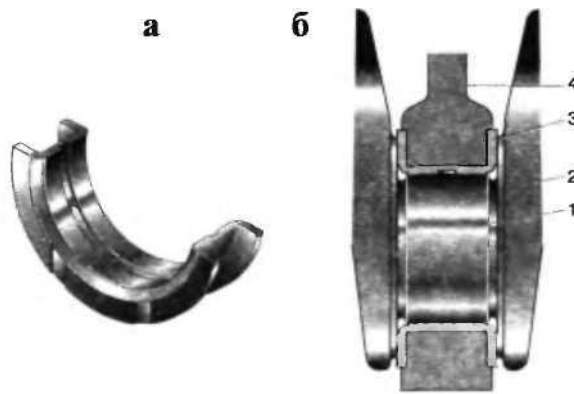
Фланцевий підшипник: а - вкладиш із завзятими фланцями; б - установка пари фланцевих вкладишів; 1 - шейку вала; 2 - щока; 3 - вкладиш; 4 - опора
